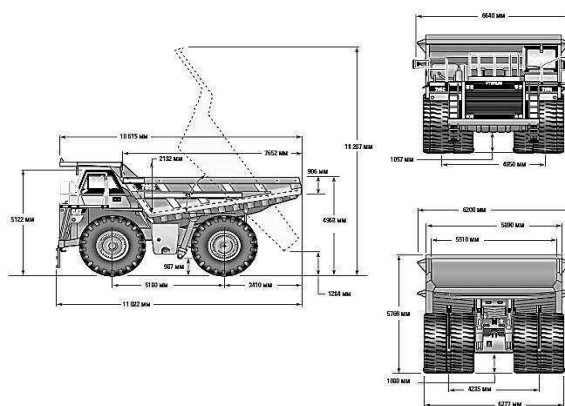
Габаритные размеры и внешний вид автосамосвал CAT 785C
